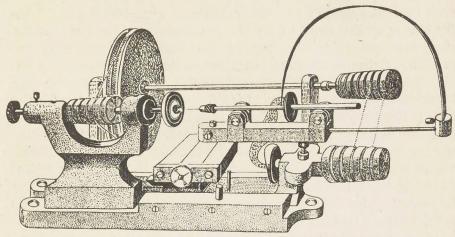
Maschine zum Ausschleifen der Bohrung des Ziehsteins.
